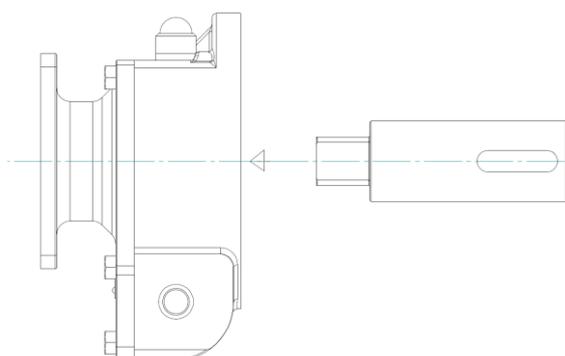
Assemblaggio dell'albero di manovra nel riduttore ILG/S
